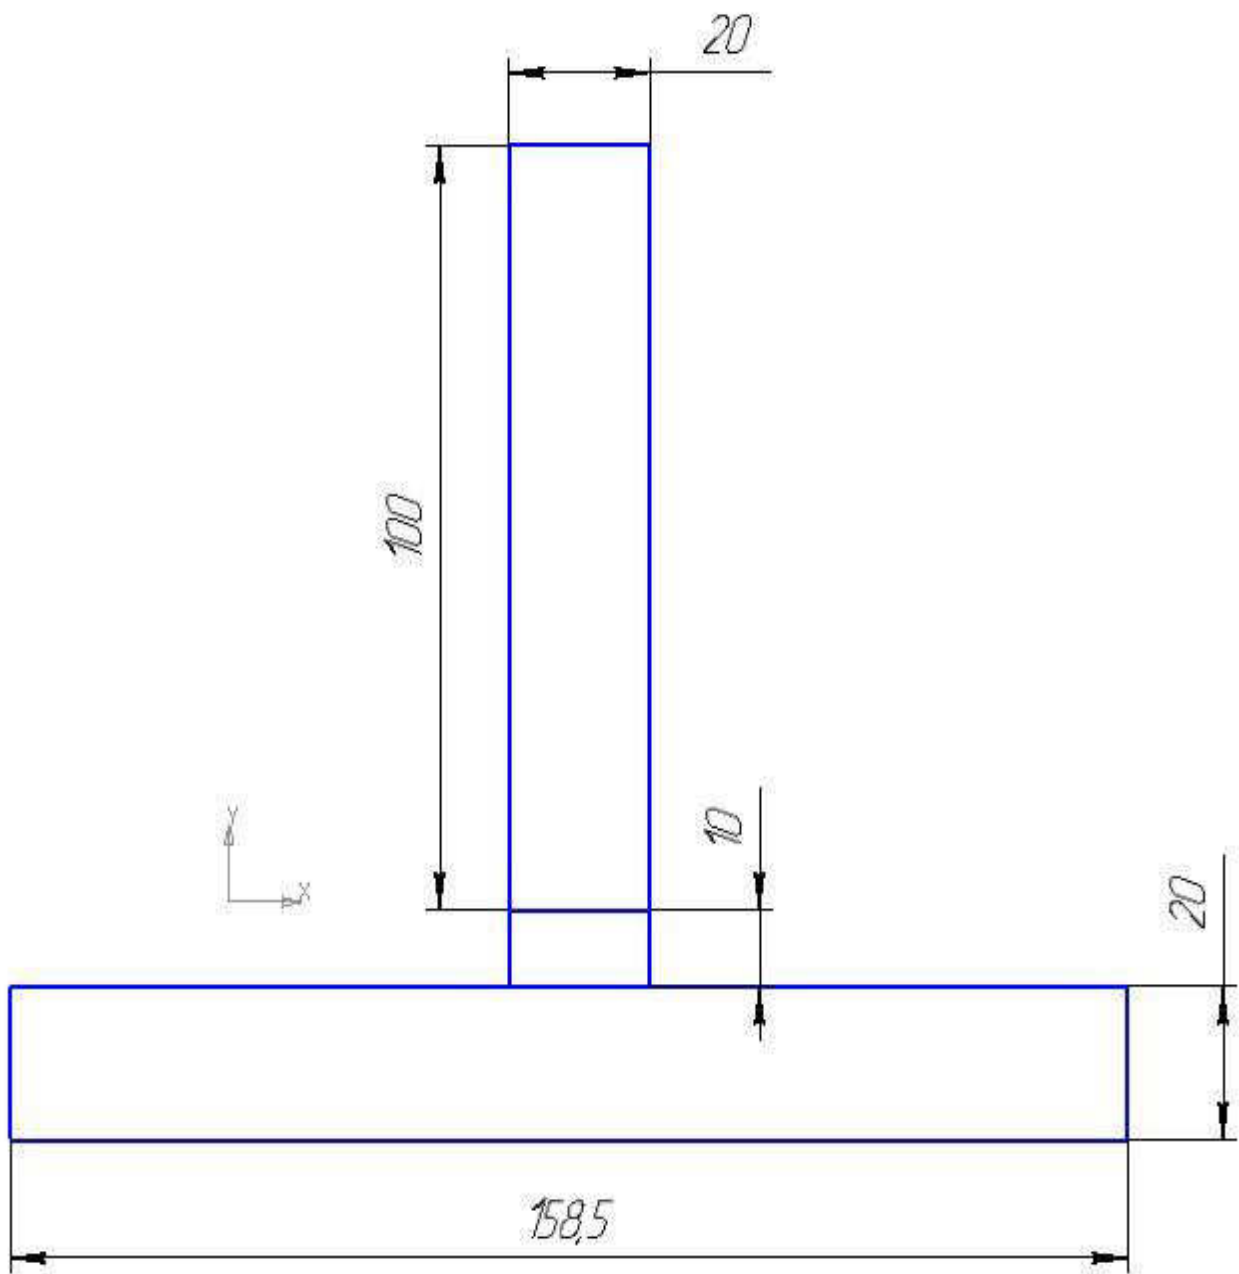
схема сварного таврового соединения без катетов
